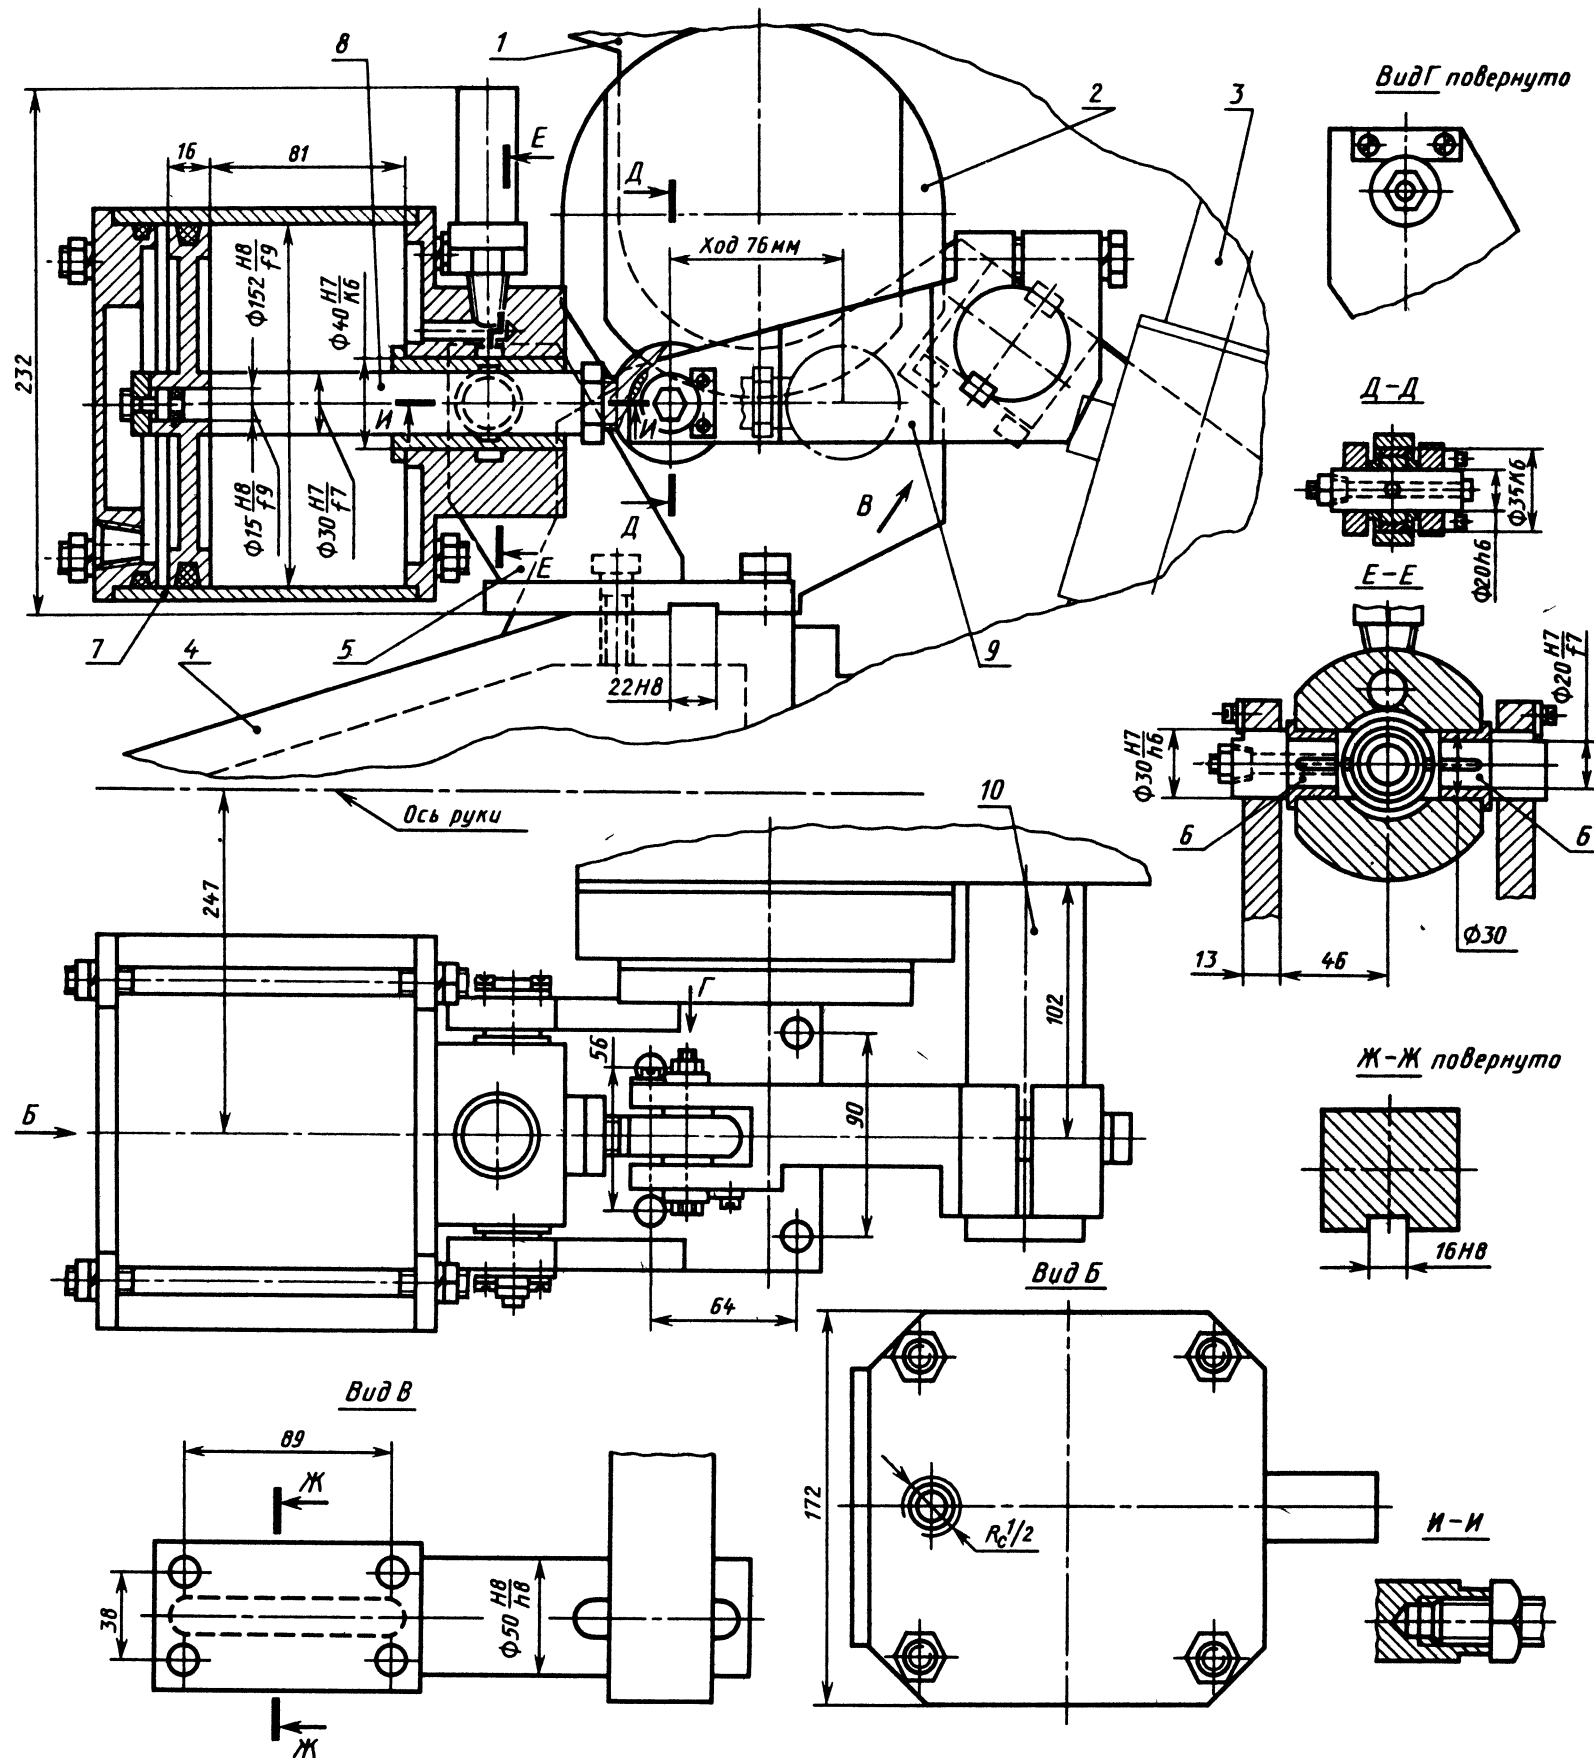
Механизм уравновешивания с пневмоцилиндром для ПР „Универсал-15”
